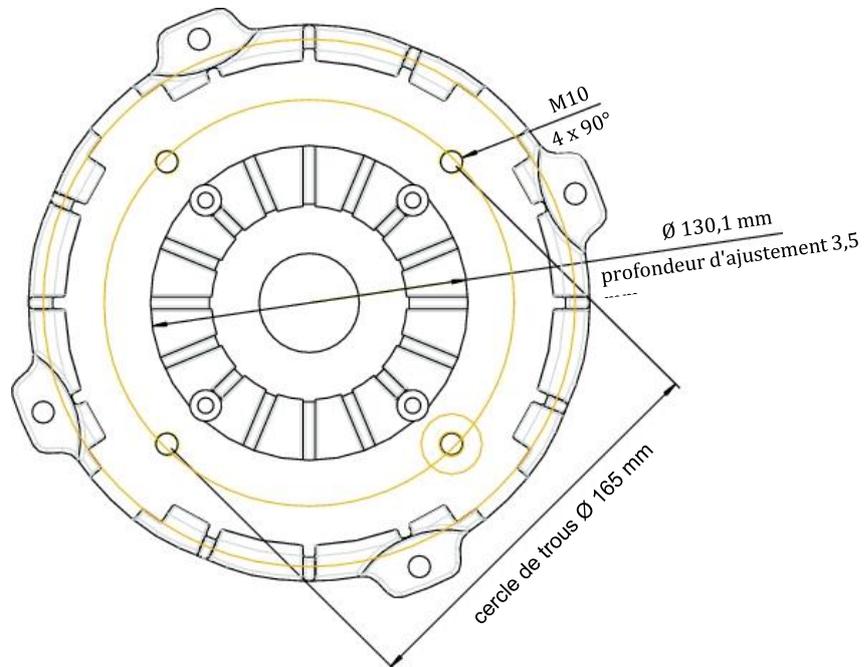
Bride pour entraînements hydrauliques et à engrenages
